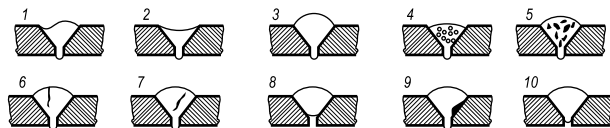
Дефекты сварных стыков: 1 — подрез; 2 — отсутствие усиления; 3 — чрезмерное усиление; 4 — пористость; 5 — шлаковые включения; 6 — наружная трещина; 7 — внутренняя трещина; 8 — непровар корня шва; 9 — боковой непровар; 10 — прожог
